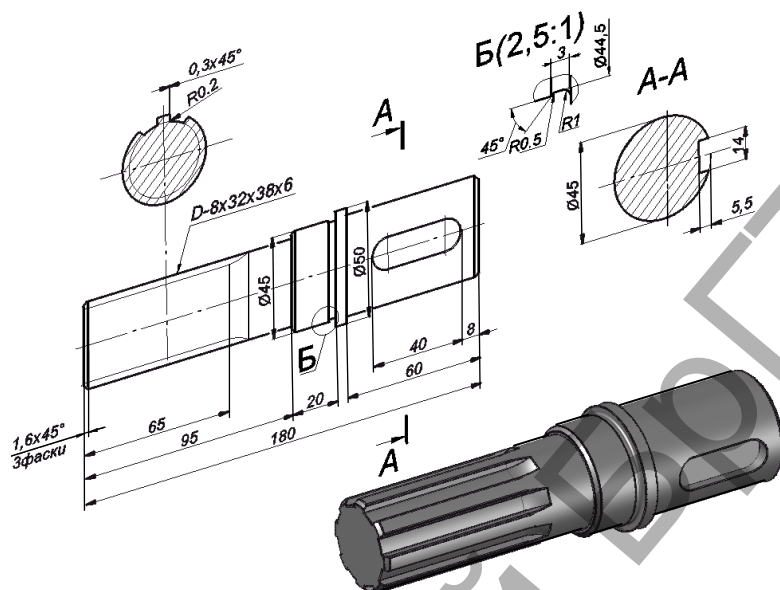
Образец формирования чертежа детали типа «Вал»
